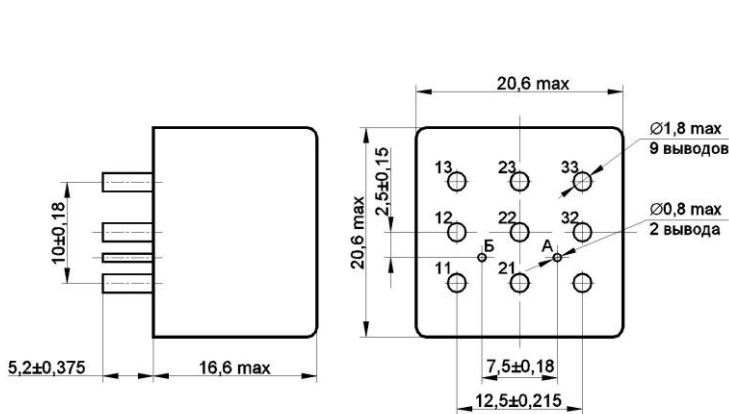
Общий вид реле исполнений РВИМ.647614.054, -01, -04, -05, -08, -10 без фланца с габаритными и присоединительными размерами
